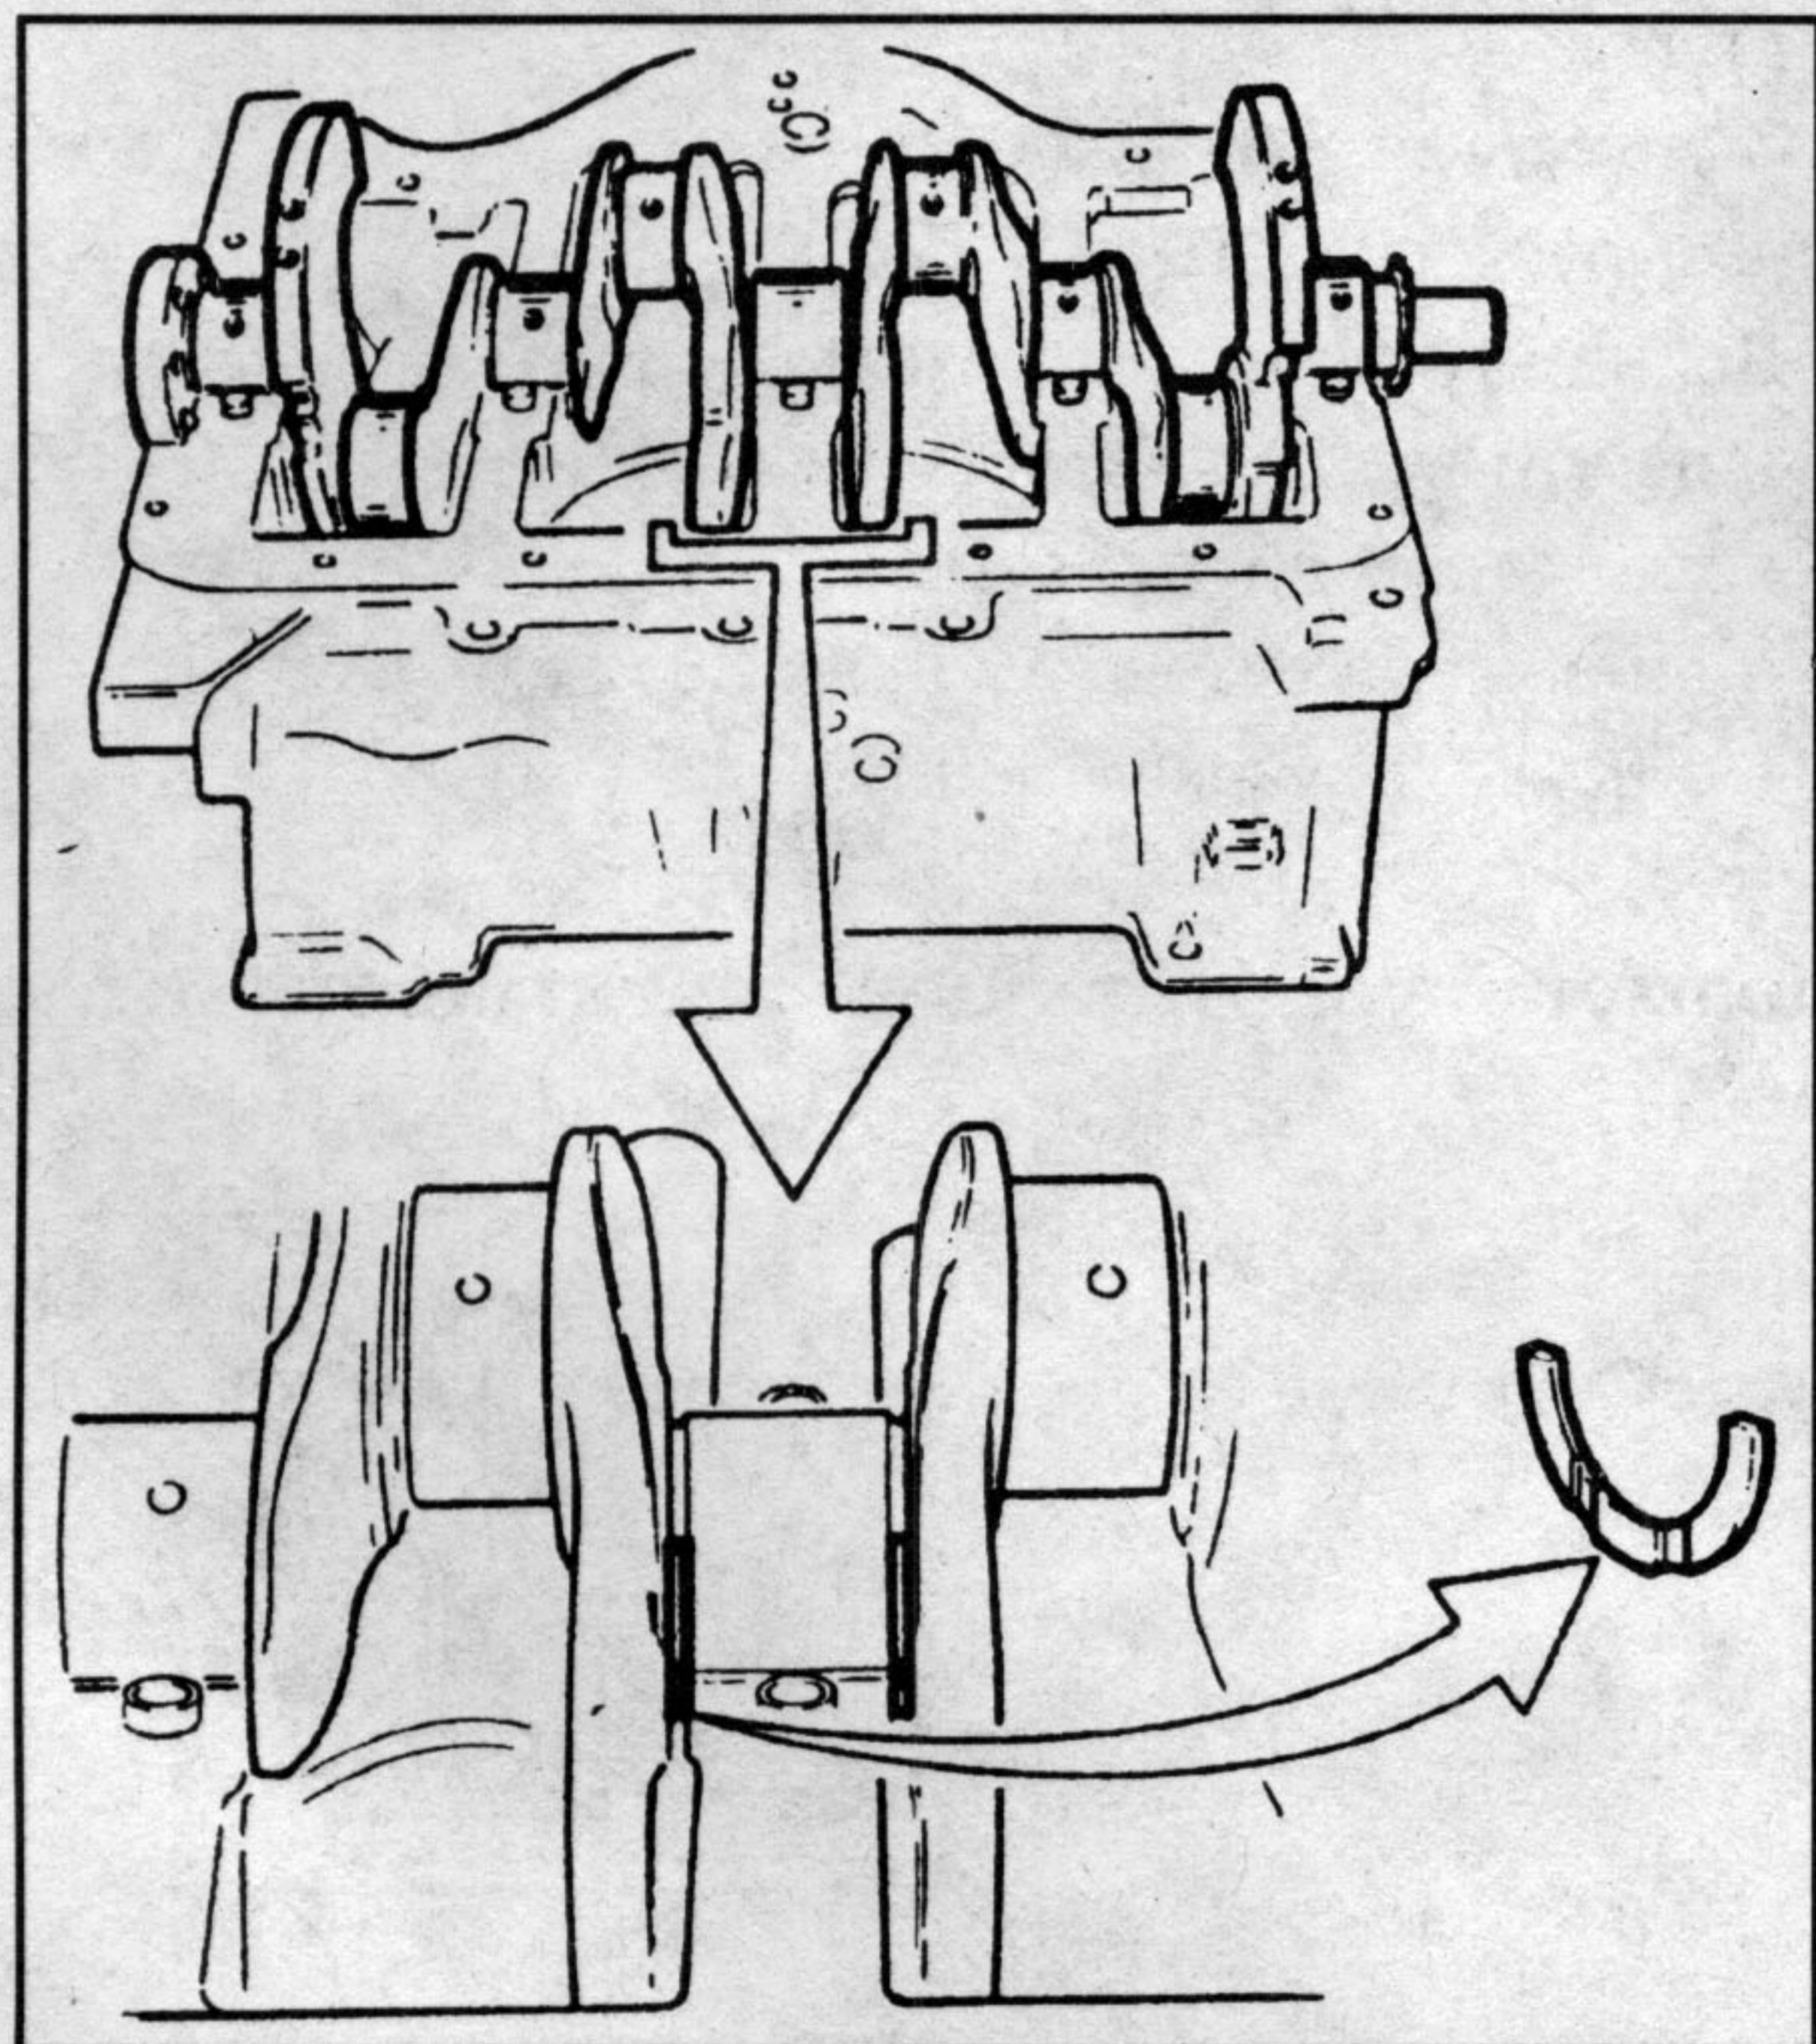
Двигатель В13/В14. Полукольца коленчатого вала и их размещение
